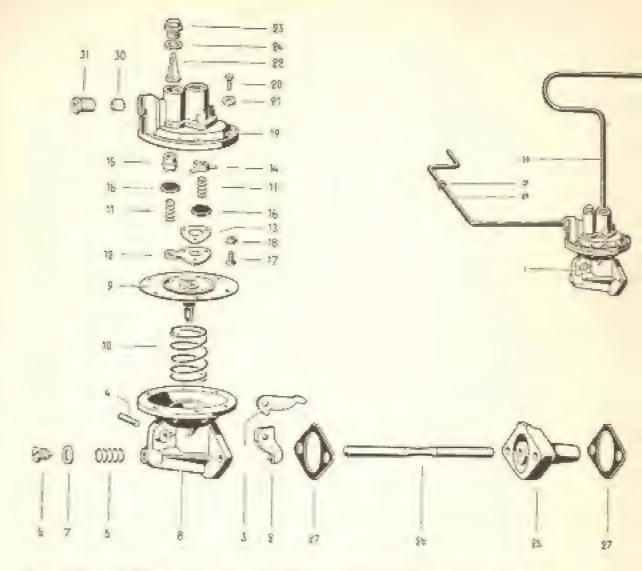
E - A bomba de gasolina montada e desmontada (Motor "1 206" - 36 HP)
